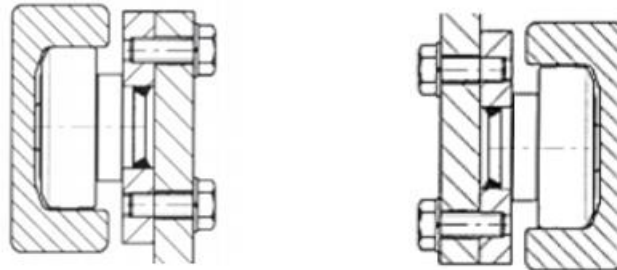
Sistema de guiado para elevación (patín y guía)
